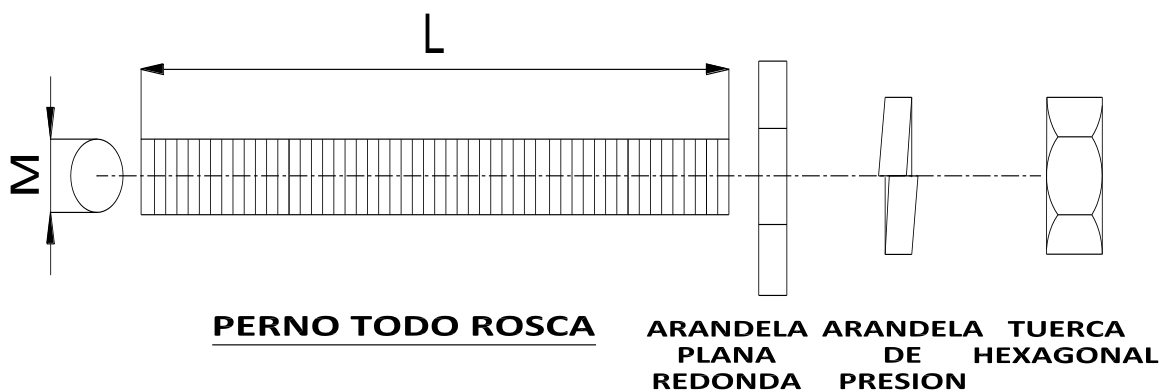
b: Herrajes para cruceta - Detalles de elementos de apriete.
